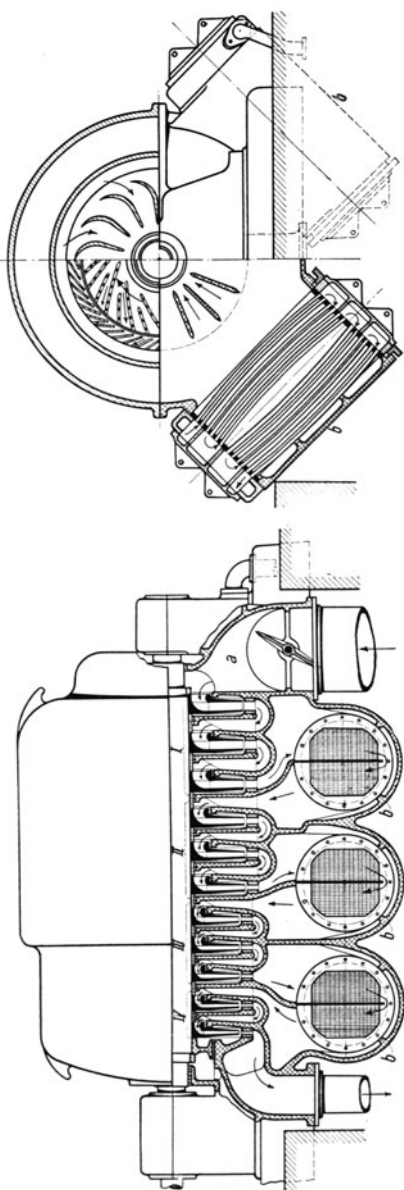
Turbokompressor mit Zwischenkühlung von Brown, Boveri & Co.
